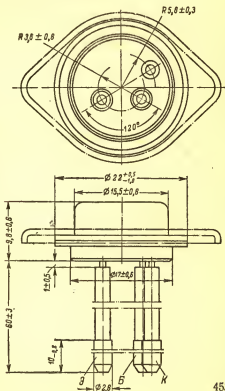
Габаритный чертеж транзисторов П605 — П606А.
